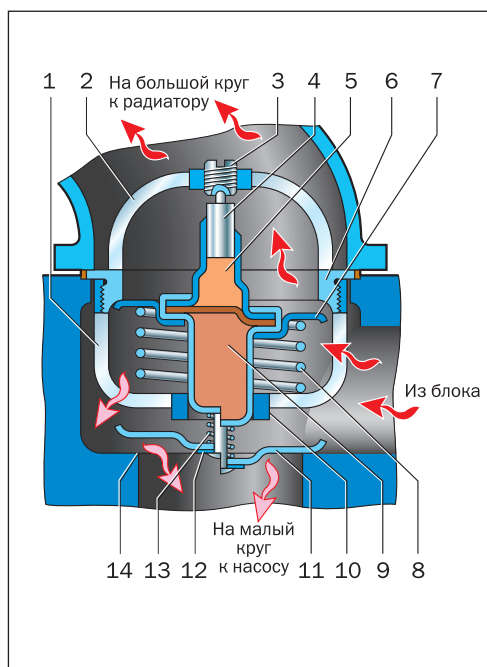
Устройство термостата с твердым наполнителем: 1 — нижняя рамка; 2 — верхняя рамка; 3 — регулировочный винт; 4 — шток; 5 — резиновая буфер-мембрана; 6 — седло основного клапана; 7 — основной клапан; 8 — пружина; 9 — капсула; 10 — направляющее кольцо; 11 — перепускной клапан; 12 — упругое кольцо; 13 — поджимная пружина; 14 — седло перепускного клапана
